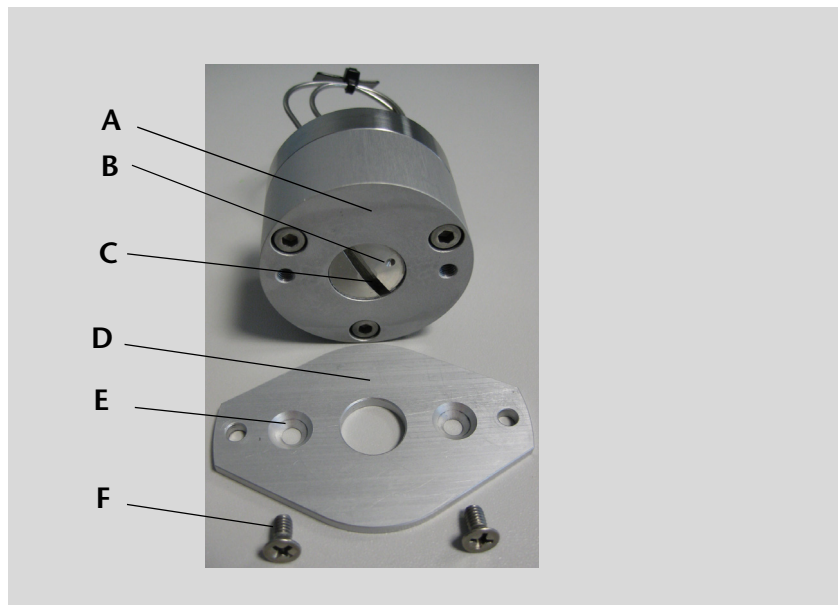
Rückseite elektrisches Ventil – Adapterplatte zur Montage
